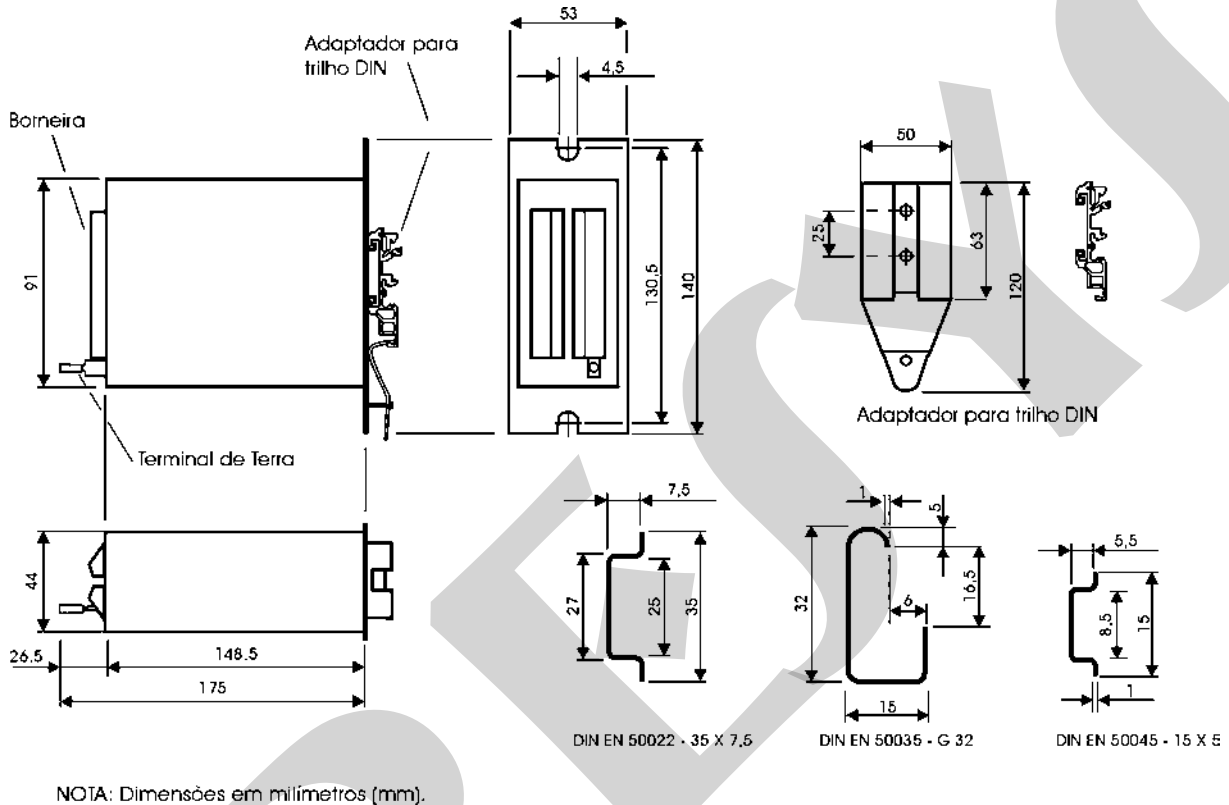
Desenho dimensional e detalhe do adaptador para trilho DIN
